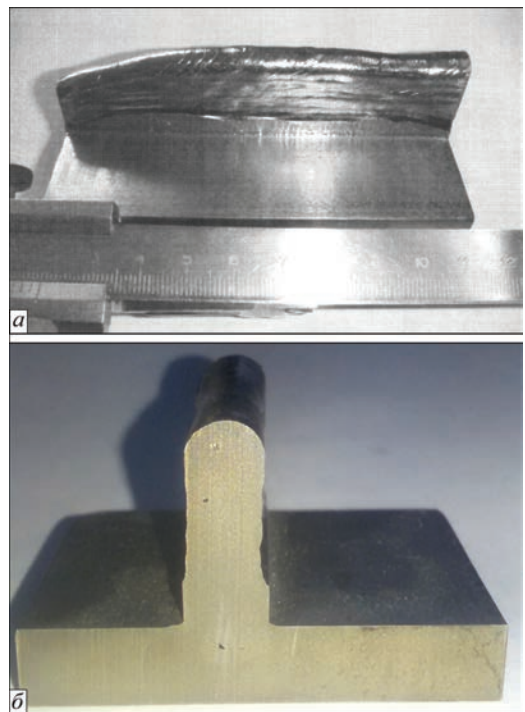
Образец детали прямолинейной формы, изготовленной электронно-лучевой 3D-наплавкой с применением периодически формирующейся ванны расплавленного металла: а — внешний вид; б — поперечное сечение прямолинейной детали
